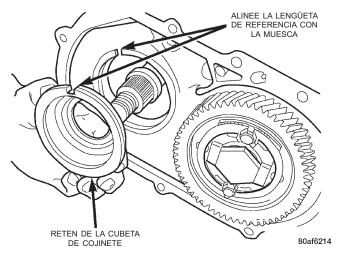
Desmontaje del retén de la cubeta de cojinete
